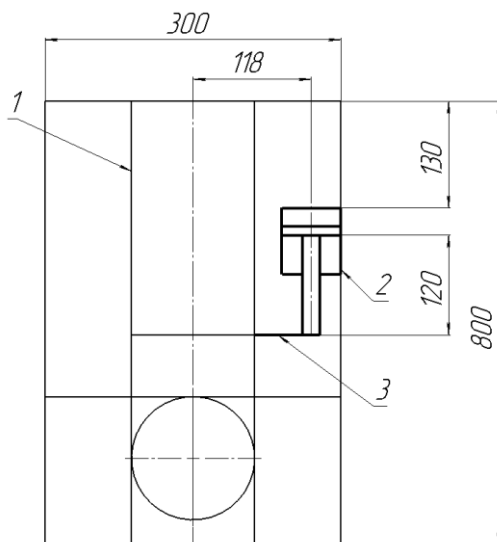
Розрахункова схема встановлення пневмоциліндру, вид зверху:
